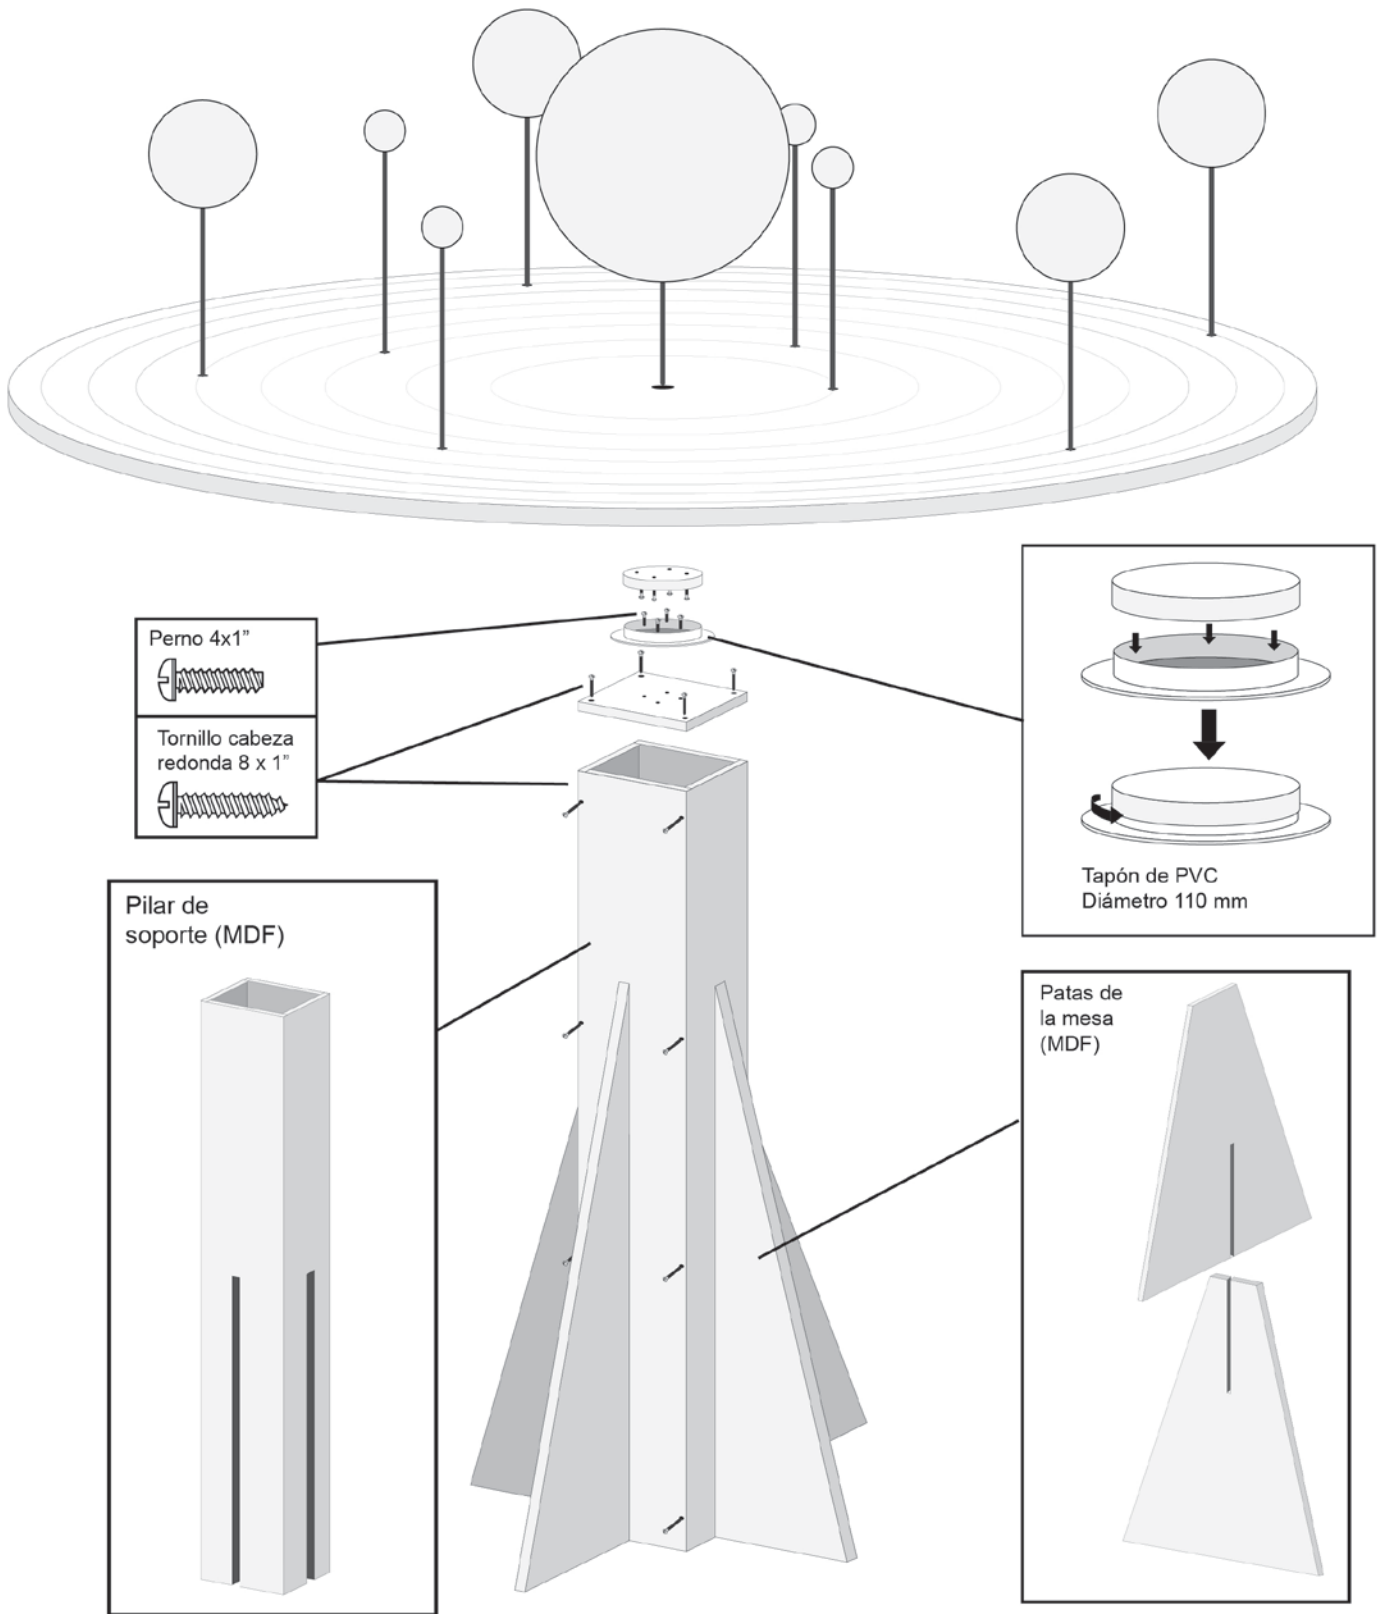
Mesa en explosión con detalles de armado, materiales y herrajes
